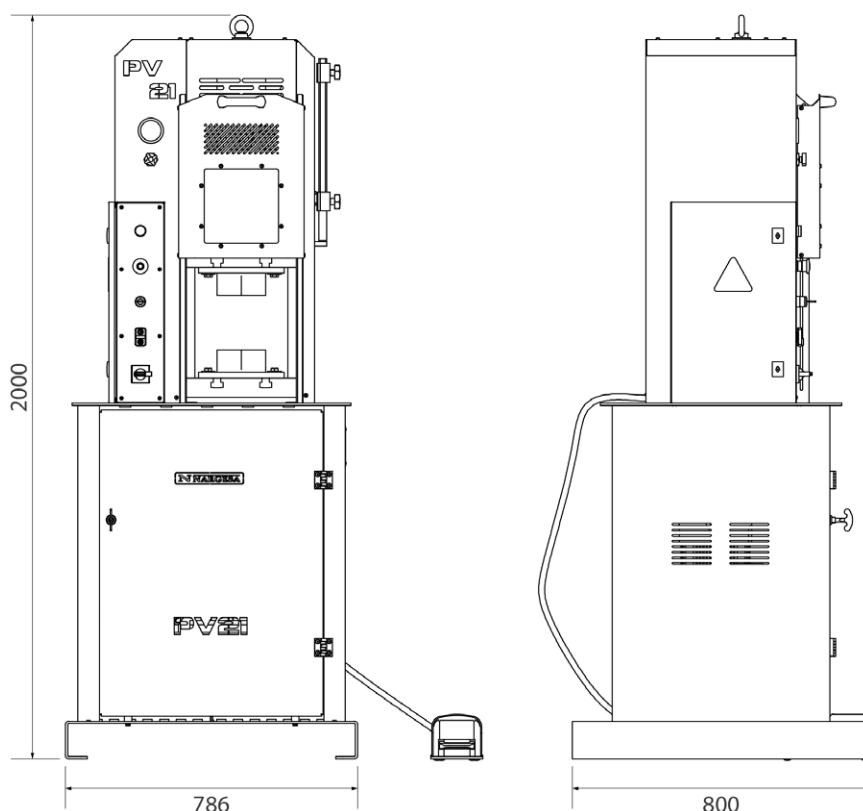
Dimensions extérieures de la butée de la Presse hydraulique pour forge PV21
